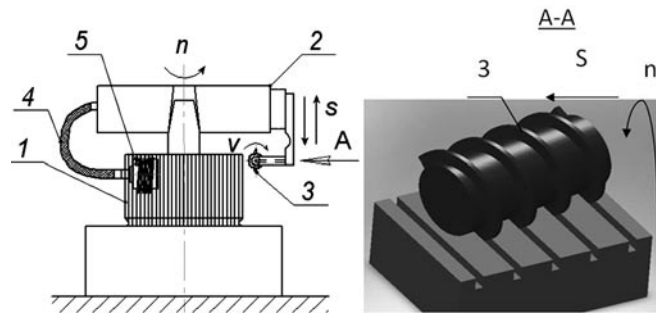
Схемы установки якоря при обработке коллектора червячной фрезой:
